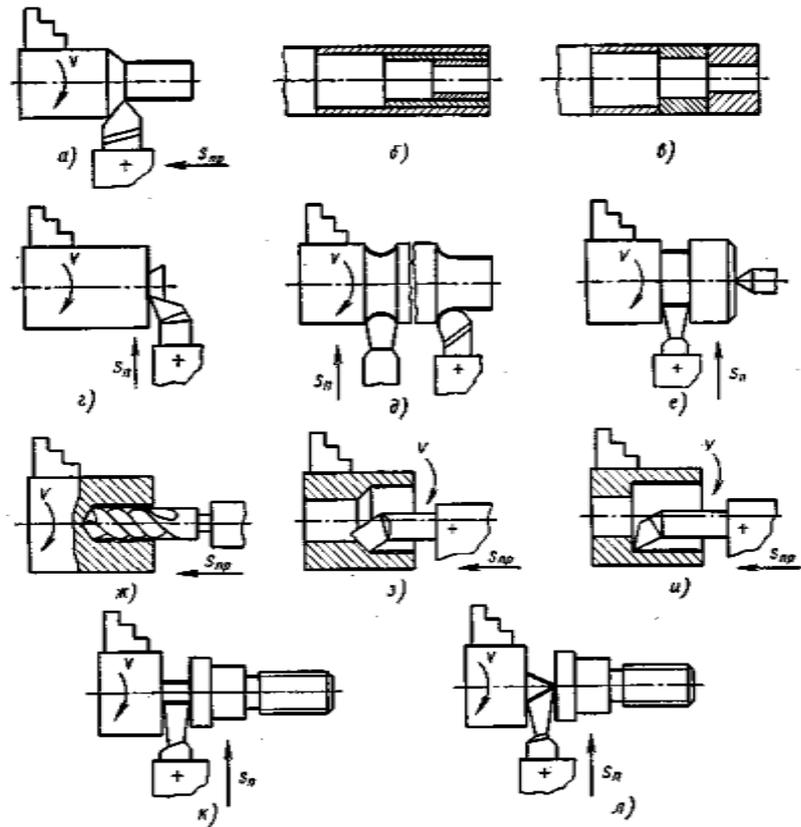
Схемы обработки заготовок на токарно-винторезном станке
